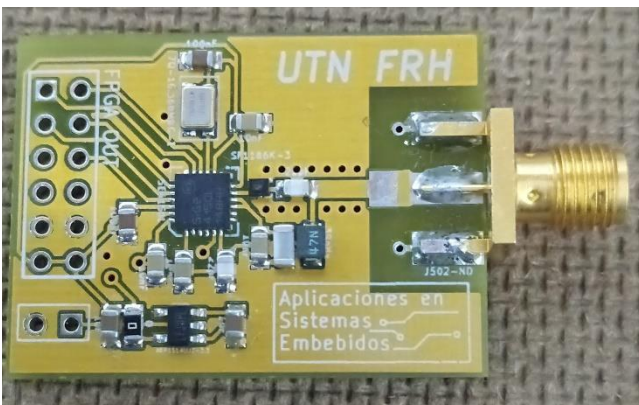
Cara superior de placa PCB del *front end* SKYWORKS 4150.
